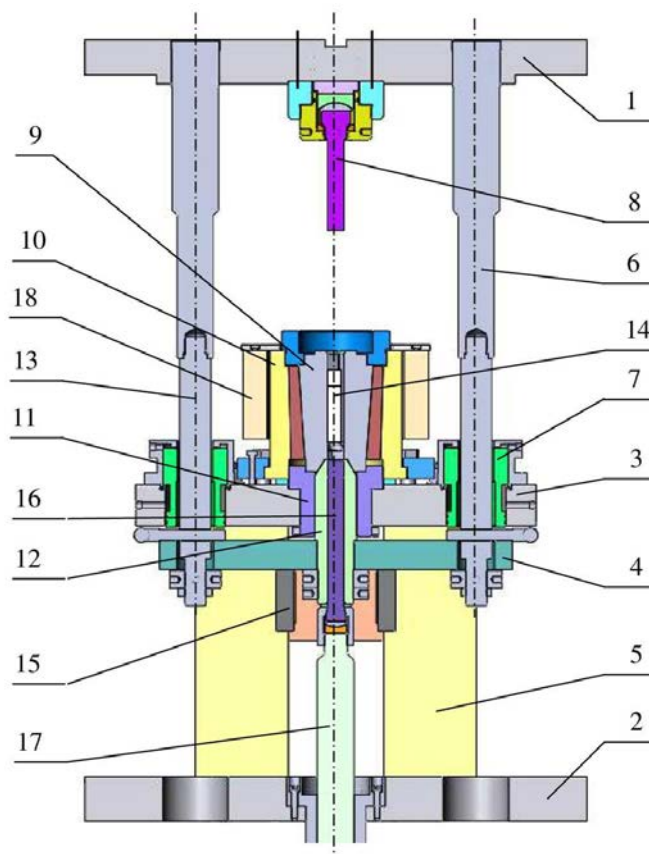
Общий вид установки для интенсивной пластической деформации порошковых заготовок методом винтовой экструзии
